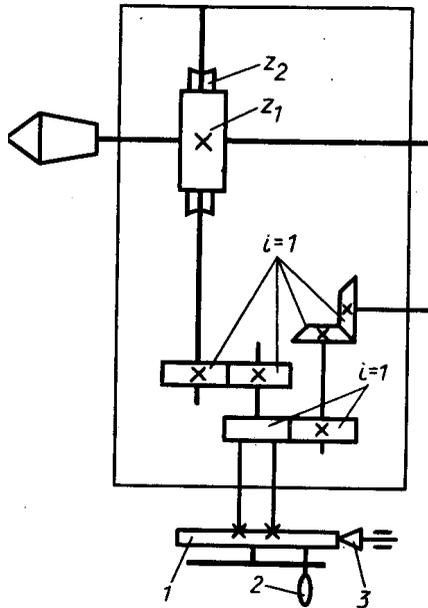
Схема наладки универсальной делительной головки на простое деление
